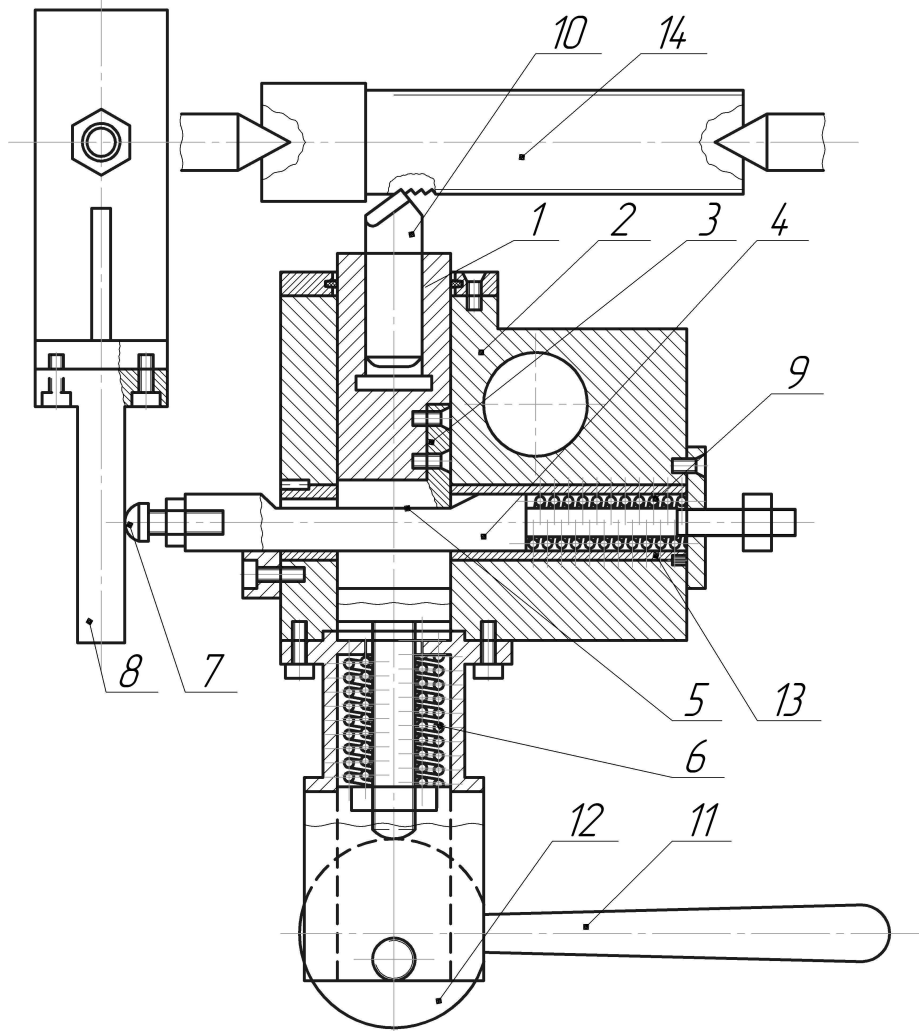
Універсальний пристрій для швидкісного нарізання різи
